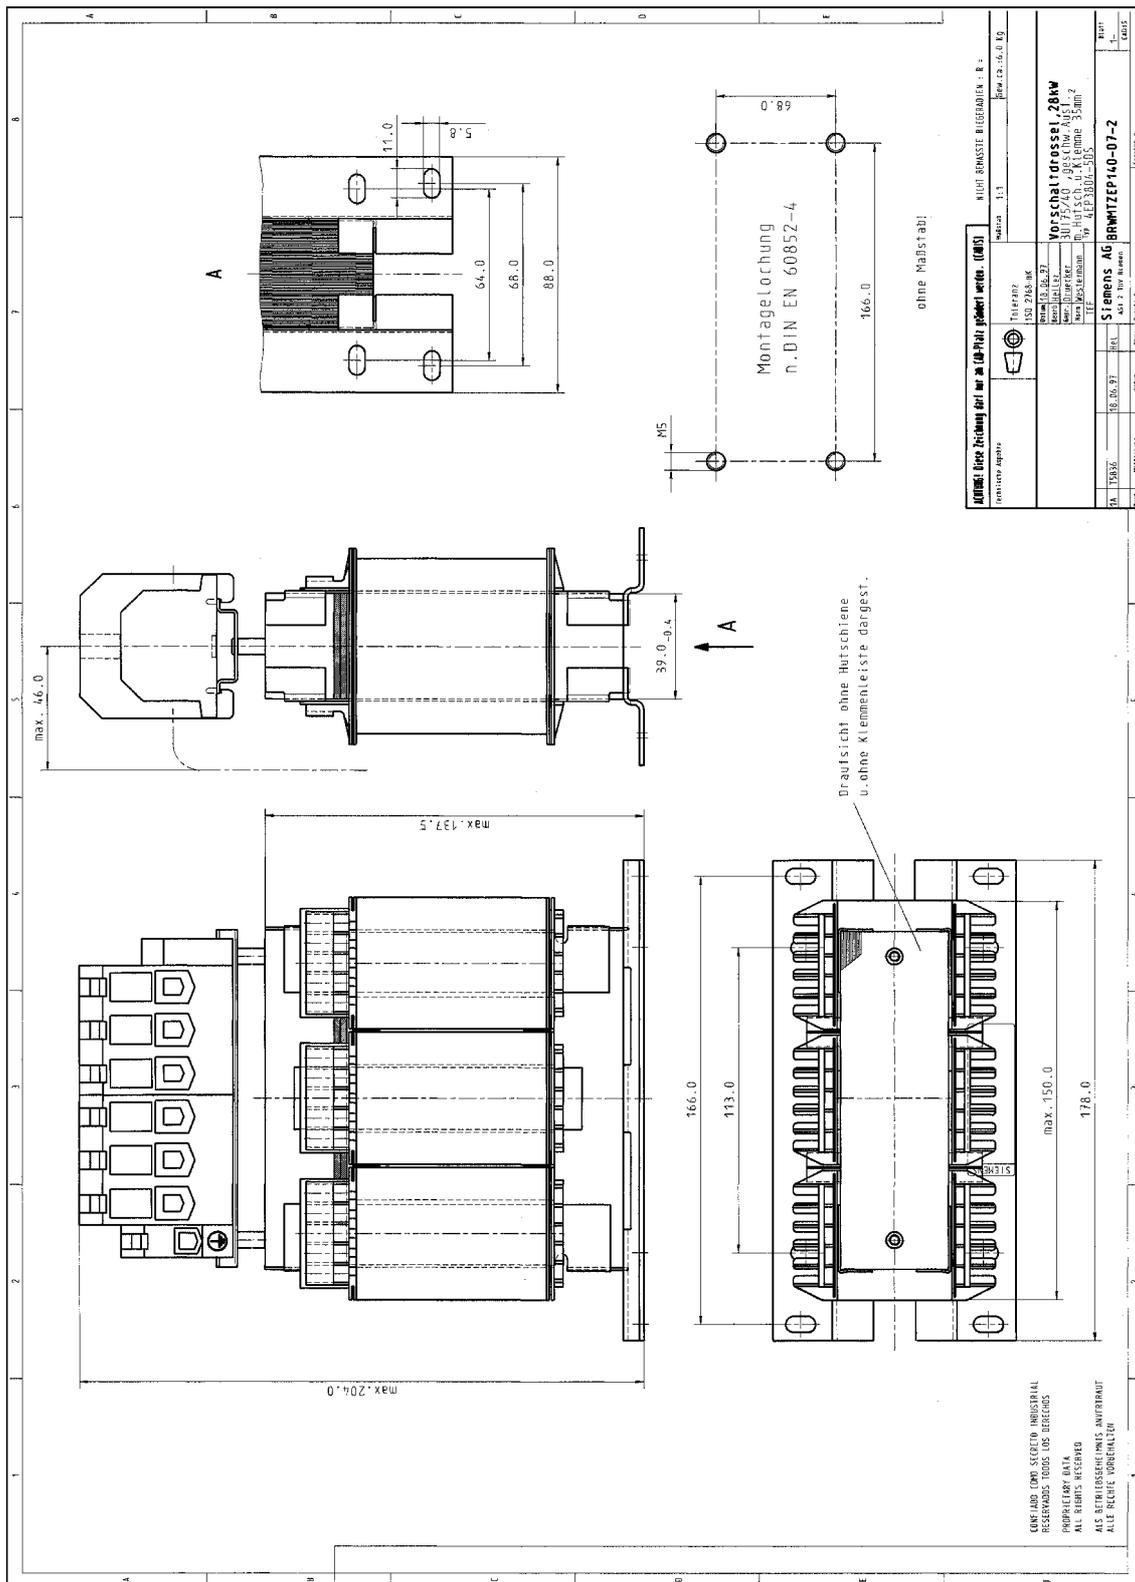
Bobina HF trifase 28 kW, 6SN1111-1AA00-0CAx
